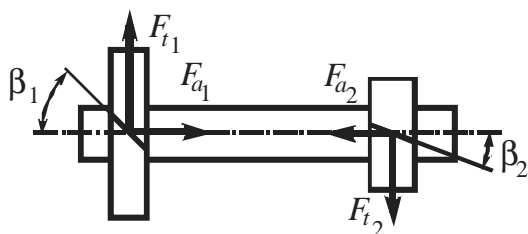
Схема сил, действующих на зубчатые колеса промежуточного вала коробки передач
